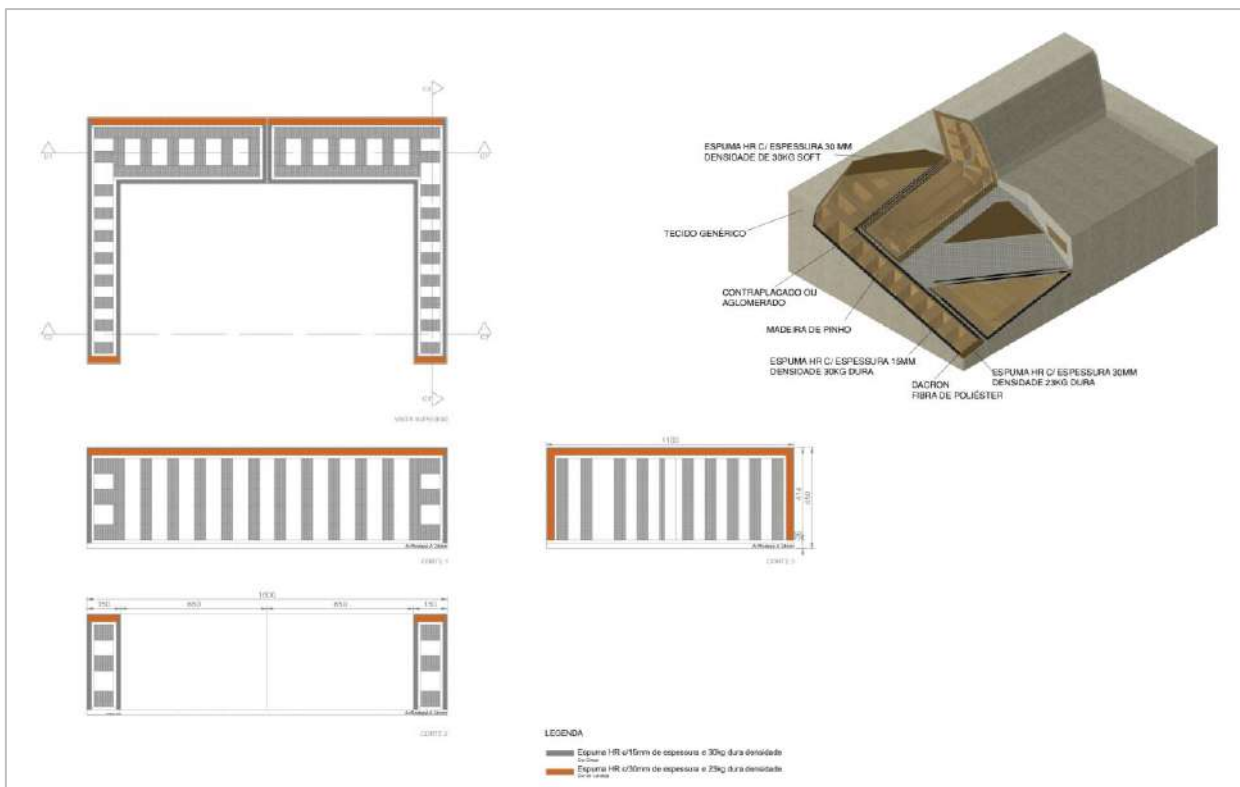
Desenhos técnicos- cortes sofá modular. Fonte: Júlia Rodrigues
